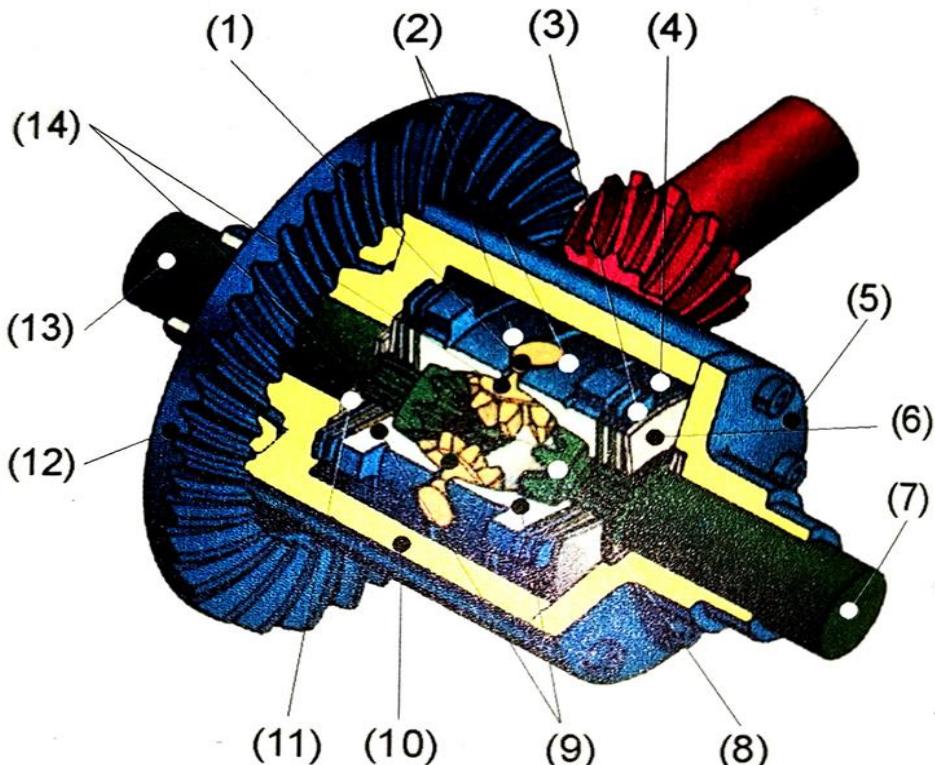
Závěr diferenciálu se zubovou spojkou [2]
